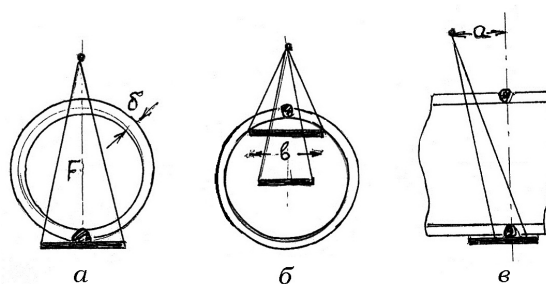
Основные схемы просвечивания сварных соединений трубопроводов
